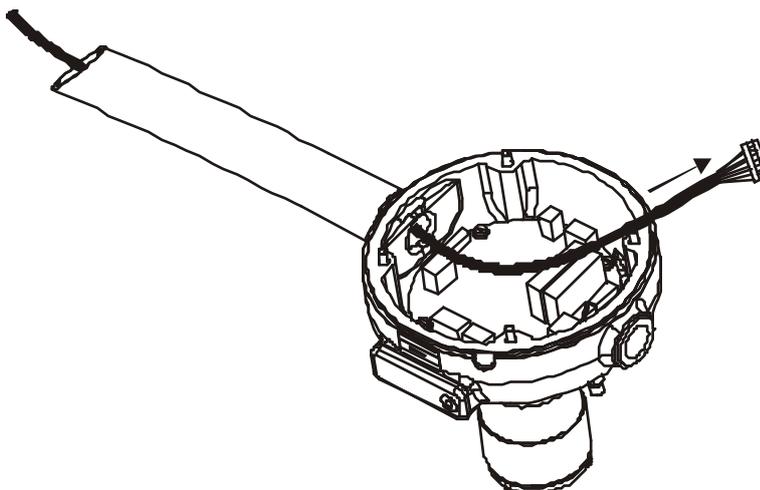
Вытягивание контрольного кабеля из трубы корпуса
